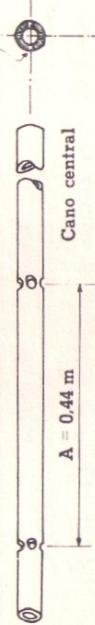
Para facilitar a soldagem, dos elementos ao mastro central, este deverá ser previamente furado conforme indicado neste desenho. A dimensão A é para o canal 9.
